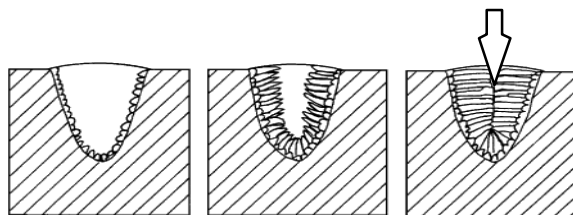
soldadura finalizada sin relleno de cráteres
